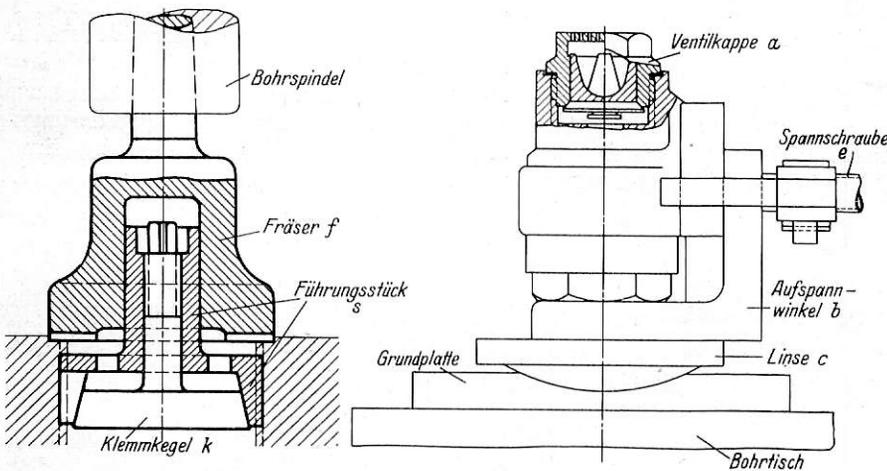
Fräser für Luftpumpen-Instandsetzung.
